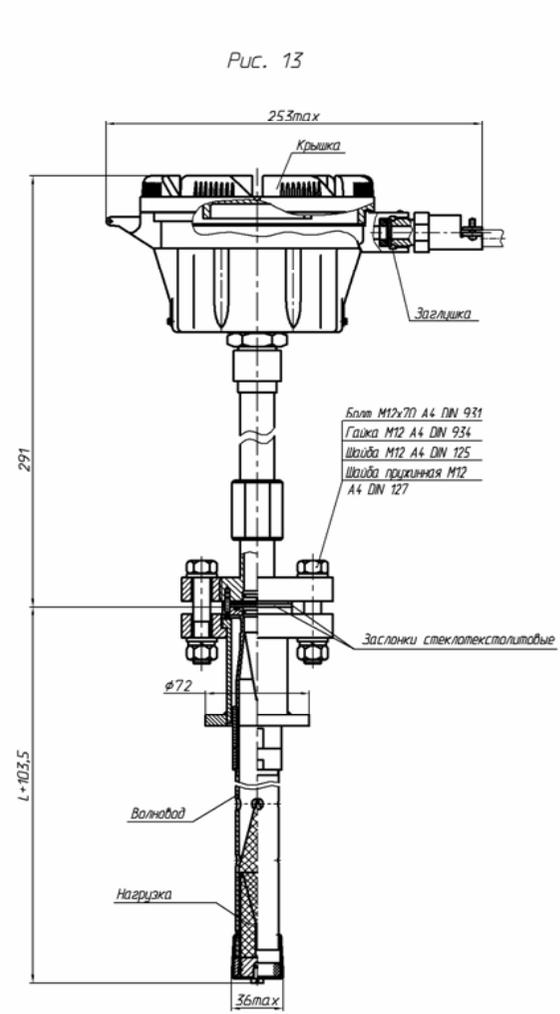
Габаритные и установочные размеры датчиков РДУЗ (лист 3)
